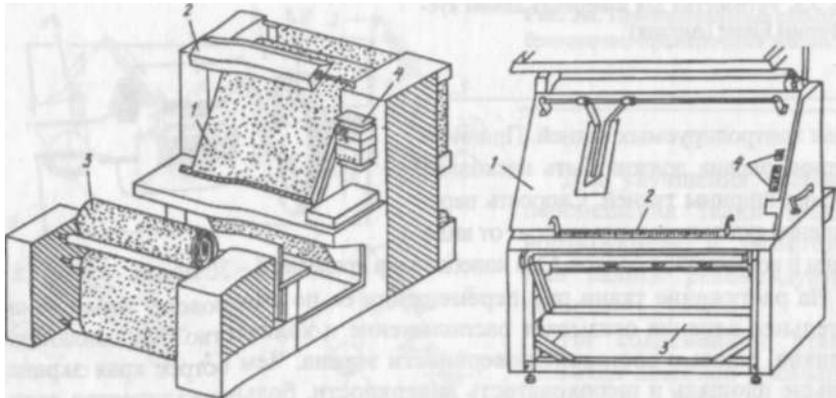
Браковочно-промерочная машина МКМ-7-180 для контроля качества, измерения длины и ширины
